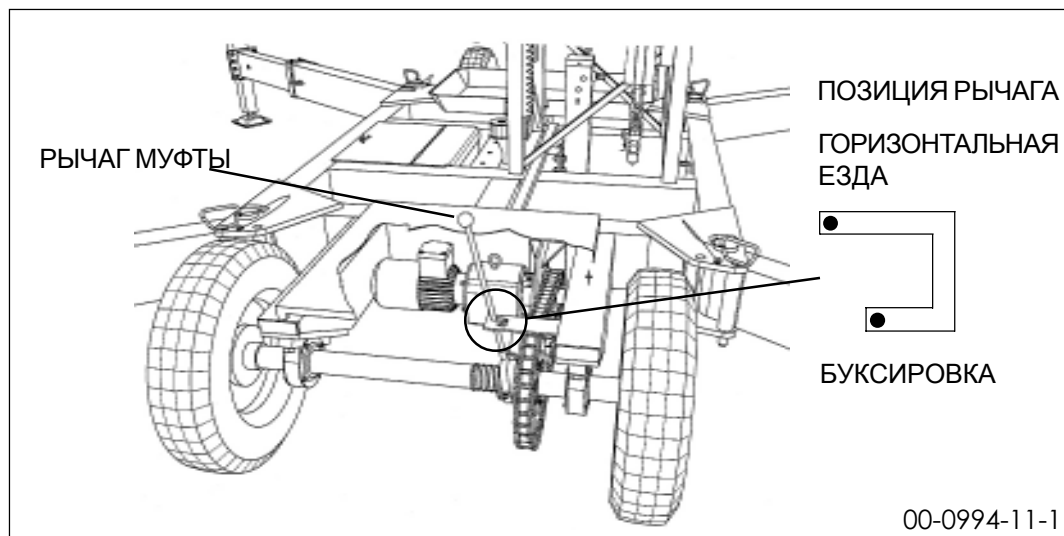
Привод езды телеги и положения рычага муфты
